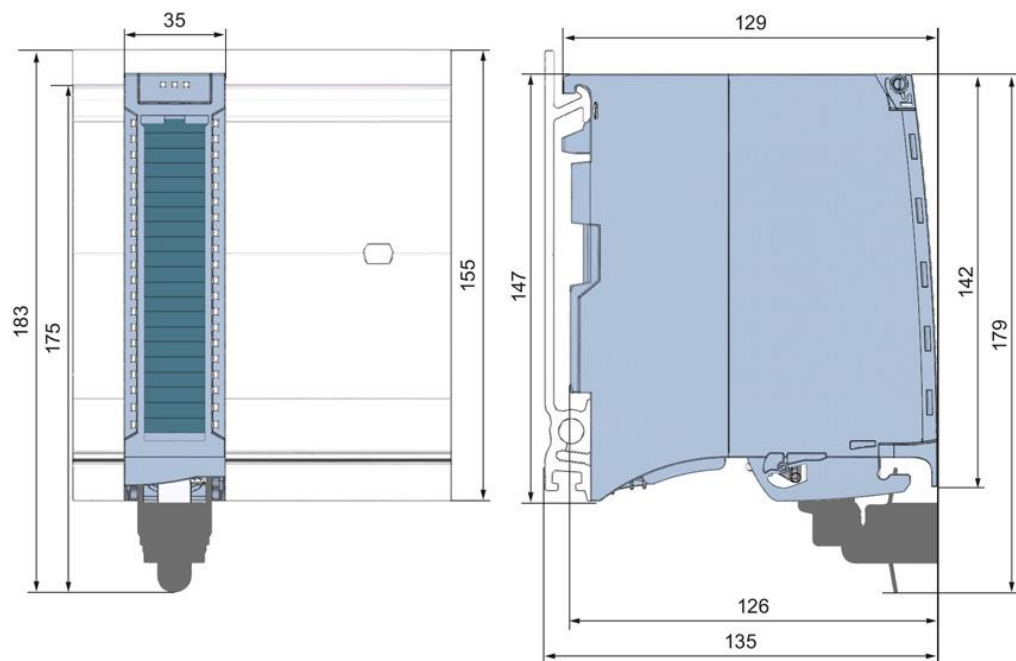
Габаритный чертеж модуля AI 8xU/I HS
